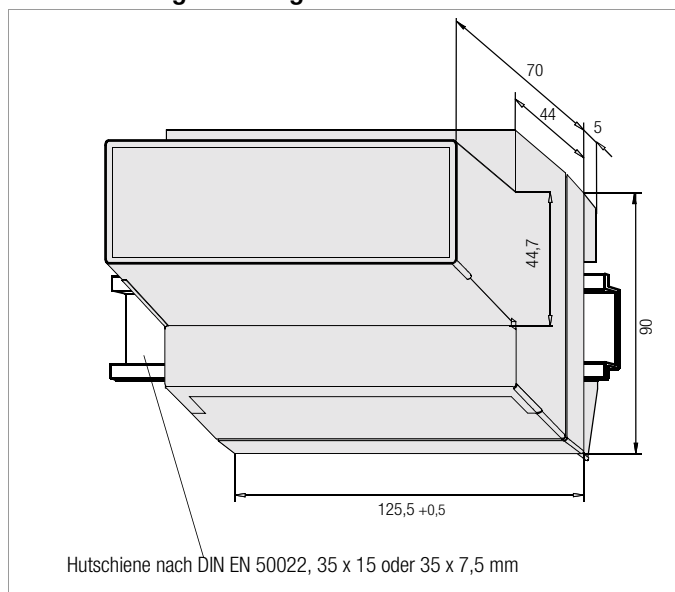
Maßzeichnung für Hutschiennenmontage (Front- und Seitenansicht)
